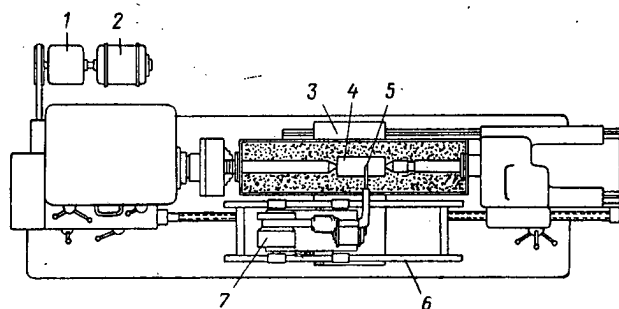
Токарный станок со сварочным аппаратом АДС-1000.
